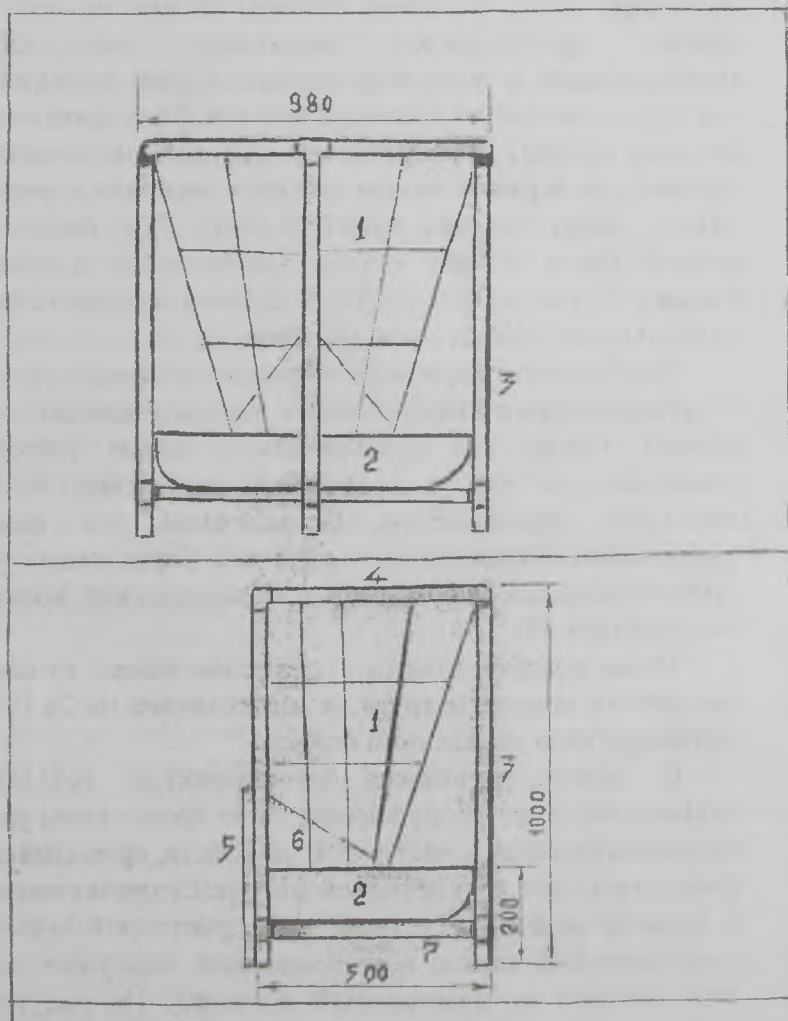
Устройство пристенной кормушки полукольцевидной формы с пластиковым каркасом. 1 - ёмкость, сетчатая, для закладки сена; 2 - шина, полукольцевидная; 3 - стойки; 4 - верхний овальный каркас; 5 - деревянный щит; 6 - конусовидное дно; 7 - нижний каркас.
